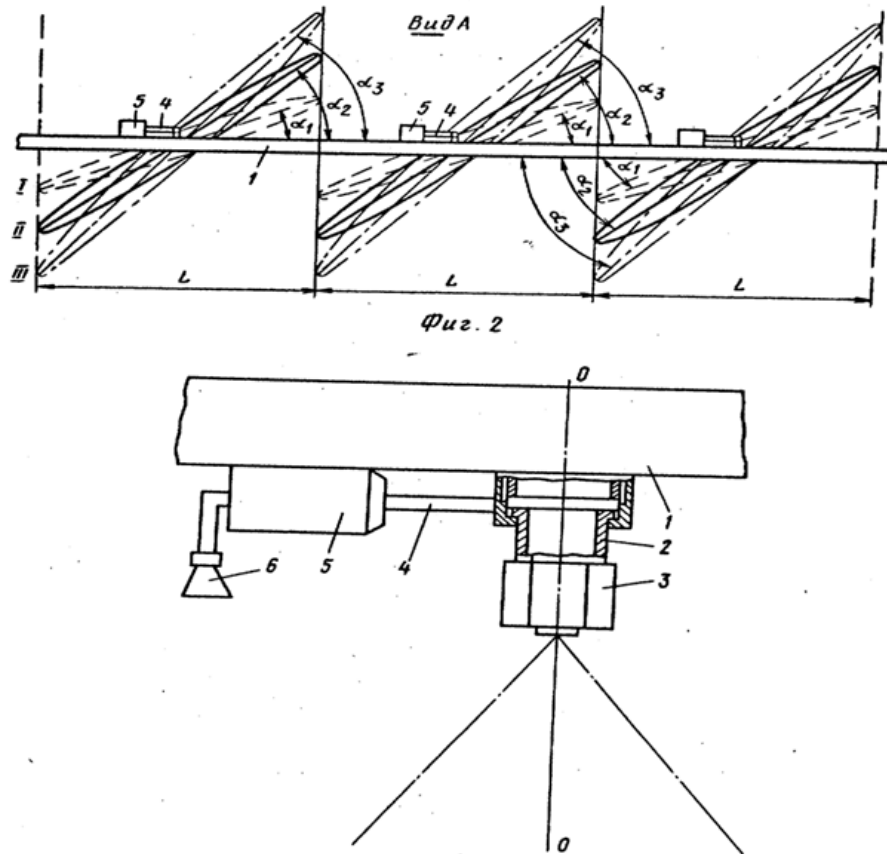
Штанговый опрыскиватель: 1 – штанга; 2 – поворотное устройство; 3 – распылитель; 4 – тяга; 5 – механизм привода; 6 – датчик [77]
